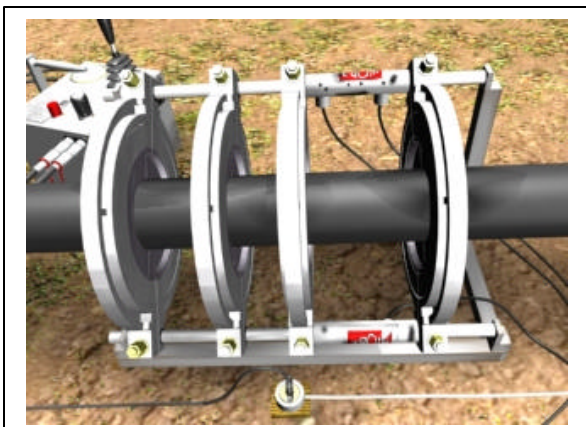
A placa de aquecimento deverá ser retirada e os tubos aproximados. O cordão de solda instantaneamente aumentará de dimensão.
